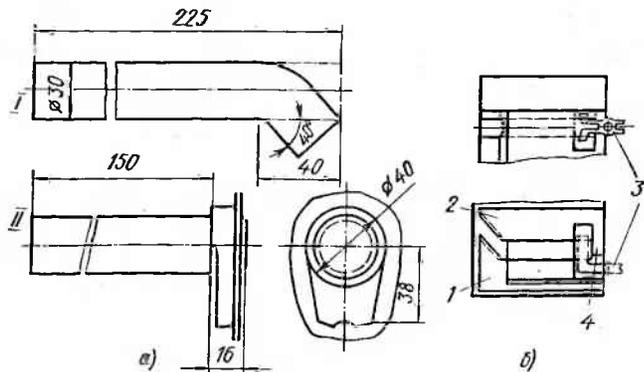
Переходы штамповки поковки с несимметричным фланцем (а) и схема гибочного ручья штампа ГКМ (б)
